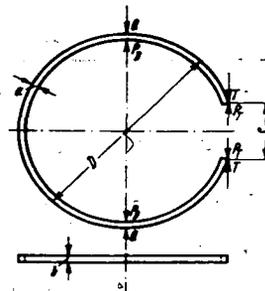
Kräfte am Kolbenring und deren Bezeichnung
